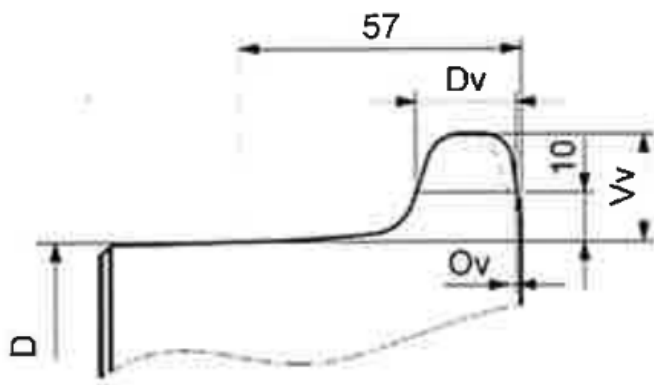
Plan mjerenja profila i geometrije gazne površine kotača
